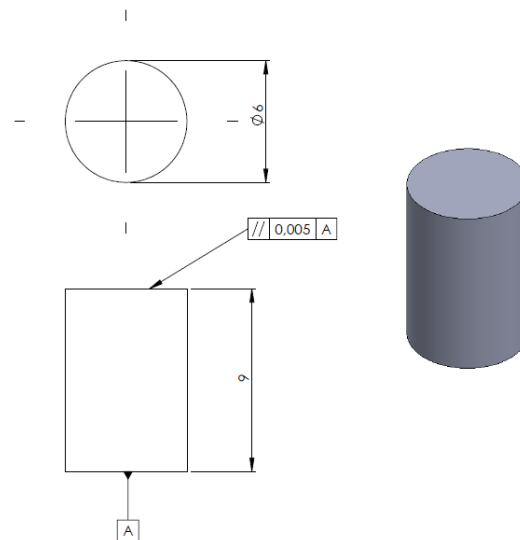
Geometria dos corpos de prova para ensaios de compressão a quente, dimensões em mm.
